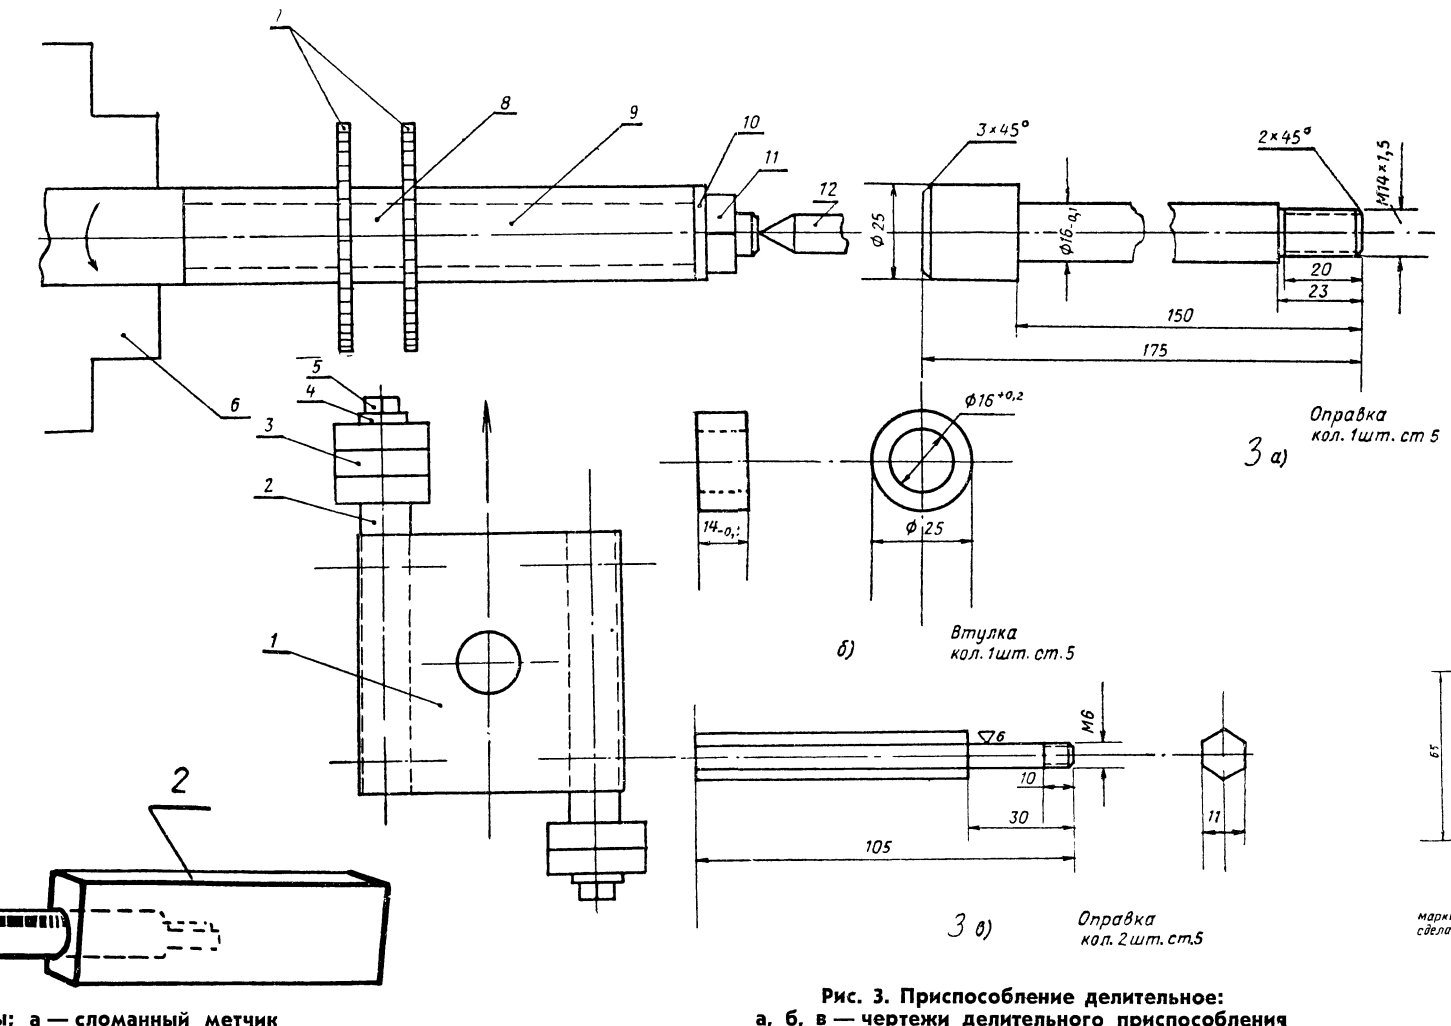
Приспособление делительное: а, б, в — чертежи делительного приспособления
